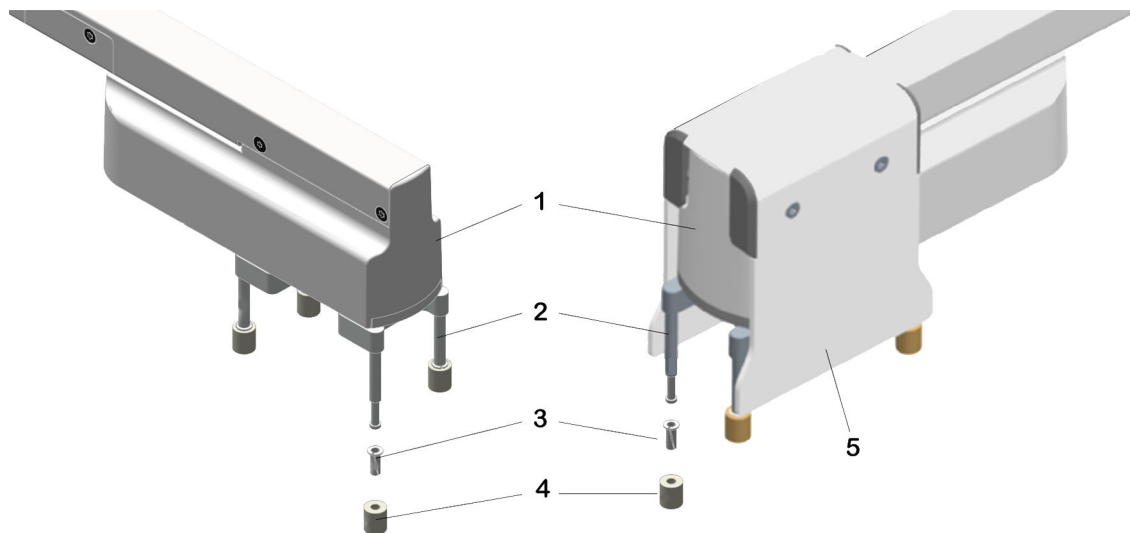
Remplacement du caoutchouc et de la douille coulissante d'un doigt
